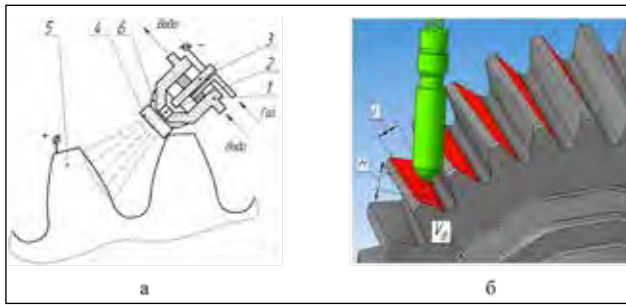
Схема пристрою: а – вид в площині обробки; б – просторовий вид процесу обробки ( $H = 45...60$  мм;  $l = 35...65$  мм)
